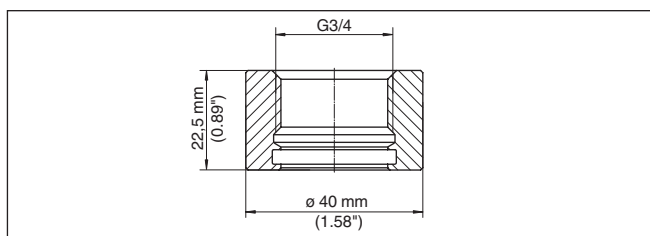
Medidas racor para soldar G $\frac{3}{4}$ (DIN 3852-X)
